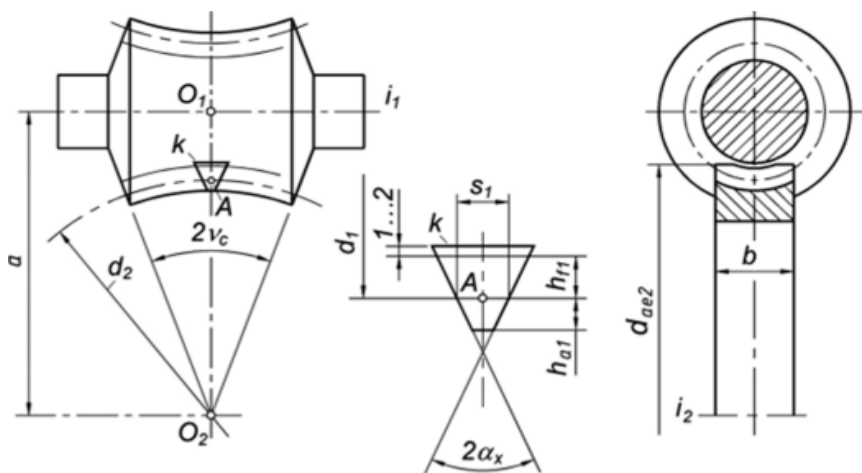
Схема червячной глобоидной передачи с линейчатым профилем винтовой поверхности
